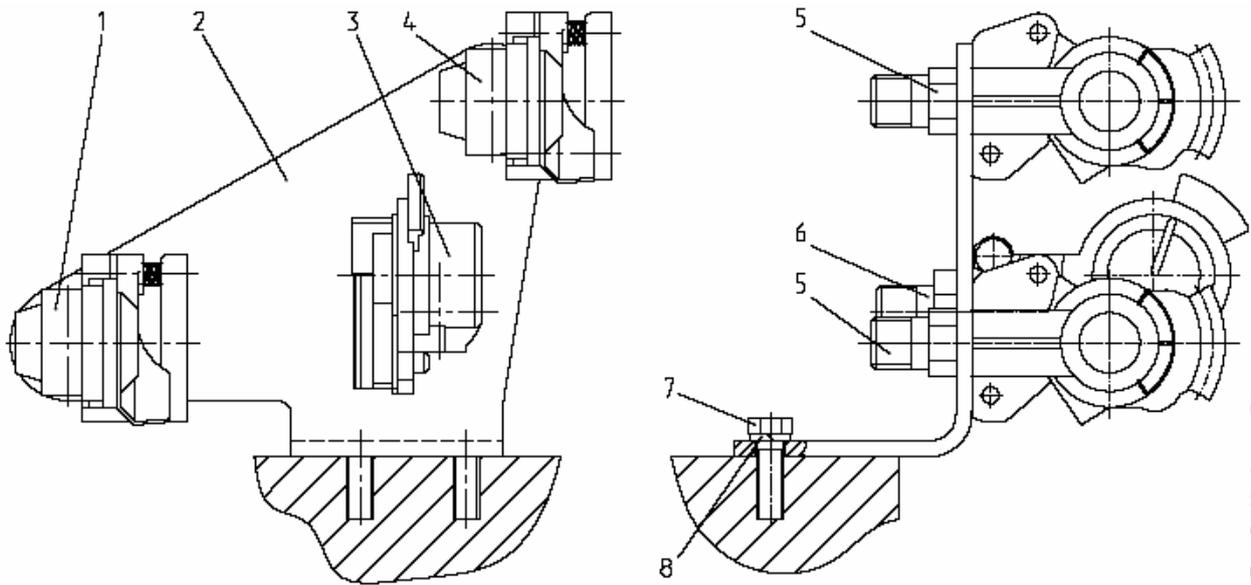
Установка головки соединительной (комбинированный пневмопривод тормозов прицепа)
